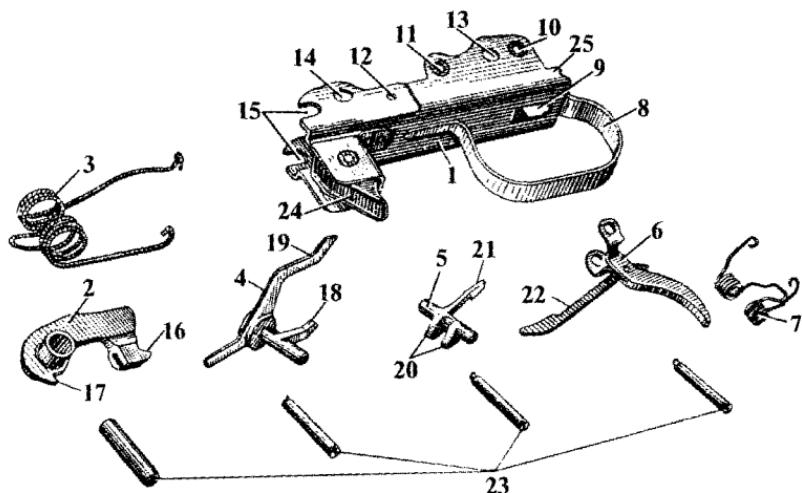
Ударно-спусковой механизм СВД-63: 1—корпус; 2—курок; 3—боевая пружина; 4—автоспуск; 5—шептало; 6—спусковой крючок; 7—пружина спускового крючка; 8—предохранительная скоба; 9 — окно для хвоста спускового крючка; 10 — отверстие для оси спускового крючка; 11—отверстие для оси шептала; 12—отверстие для оси автоспуска; 13—отверстие для оси предохранителя; 14—отверстие для оси курка; 15—вырезы для оси перемычки; 16—боевой взвод; 17—взвод автоспуска; 18—шептало автоспуска; 19—рычаг автоспуска; 20—зацепы шептала; 21—хвост шептала; 22—тяга спускового крючка; 23—оси; 24—зашелка магазина; 25—зашеп для конца пружины спускового крючка.
